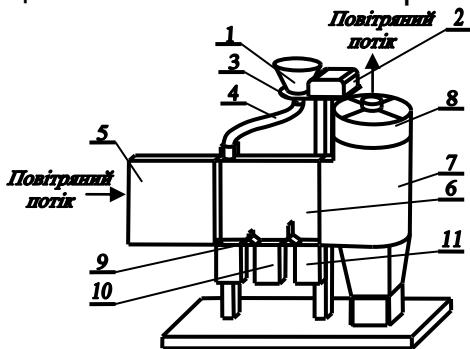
Калібратор яєць зернової молі: 1 – бункер; 2 – вібраційний пристрій; 3 – дозатор; 4 – стабілізуючий патрубок; 5 – повітряний колектор; 6 – камера розділення; 7 – циклонний сепаратор; 8 – вентилятор витяжного типу; 9, 10, 11 – контейнери.
